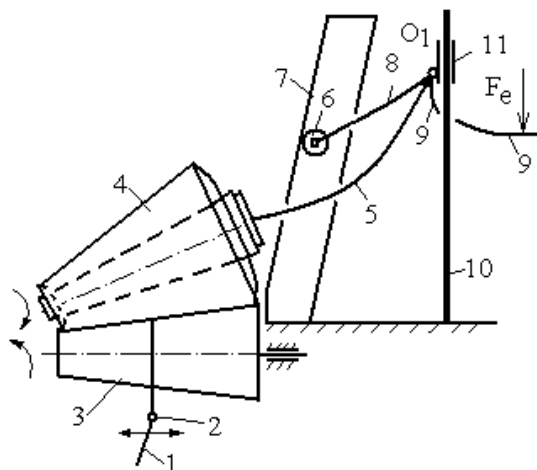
Mecanismul de obținere a bobinelor cu bază sferică
